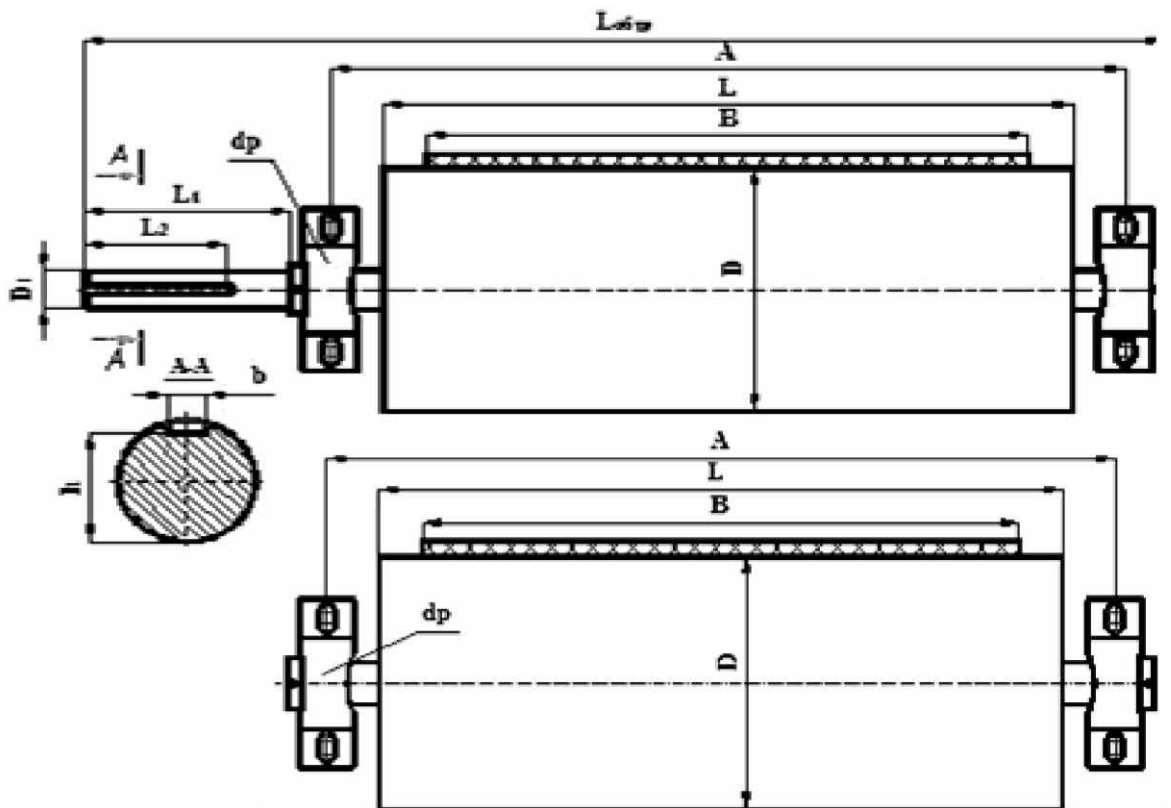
Барабан приводний, непривідний: - ширина стрічки; D – діаметр барабана; $D1$ – діаметр валу; $L_{заг}$ - загальна довжина валу; L – довжина обічайки барабана; $L1$ – довжина консолі; $L2$ – довжина шпонки; dp – діаметр підшипника; A – приєднувальний розмір до рами конвеєра.
